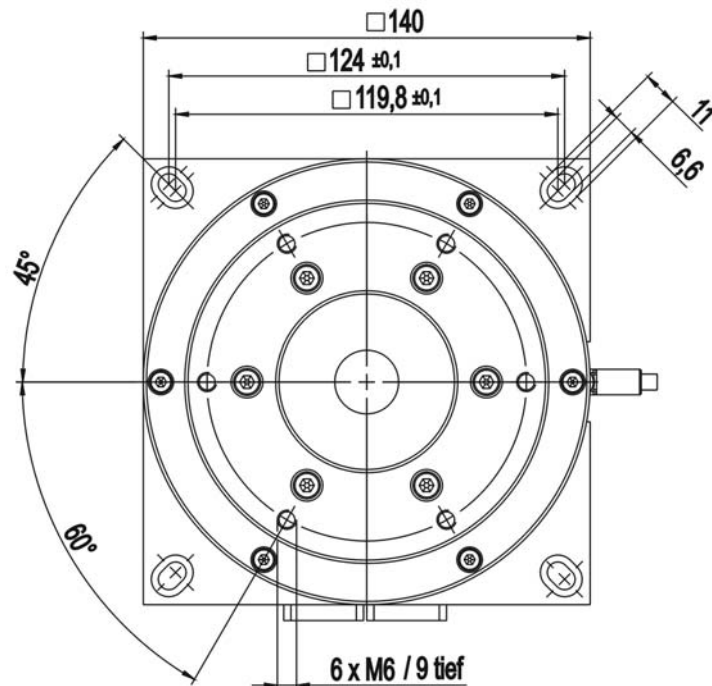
Position der Befestigungsbohrungen (Ansicht von oben)
